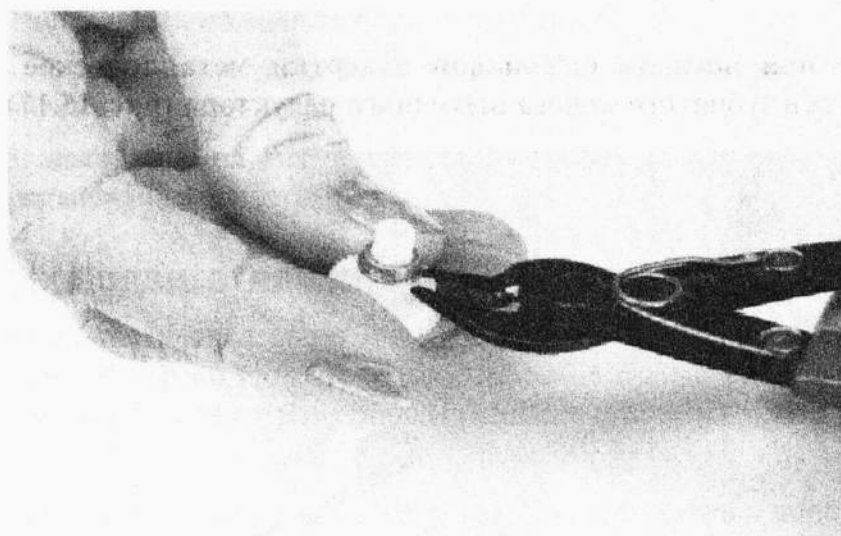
Осторожно откусите стопор на колесе выходного редуктора
